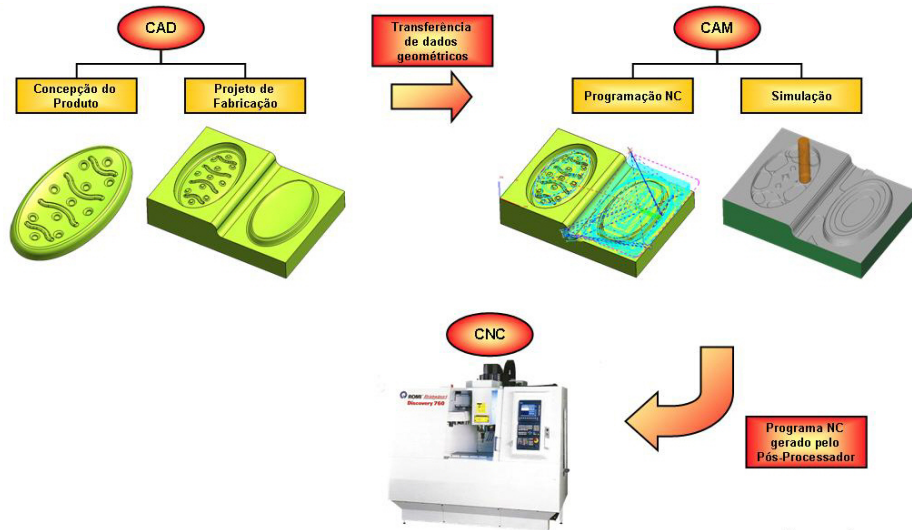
Integração CAD/CAM/CNC na manufatura de superfícies complexas.
